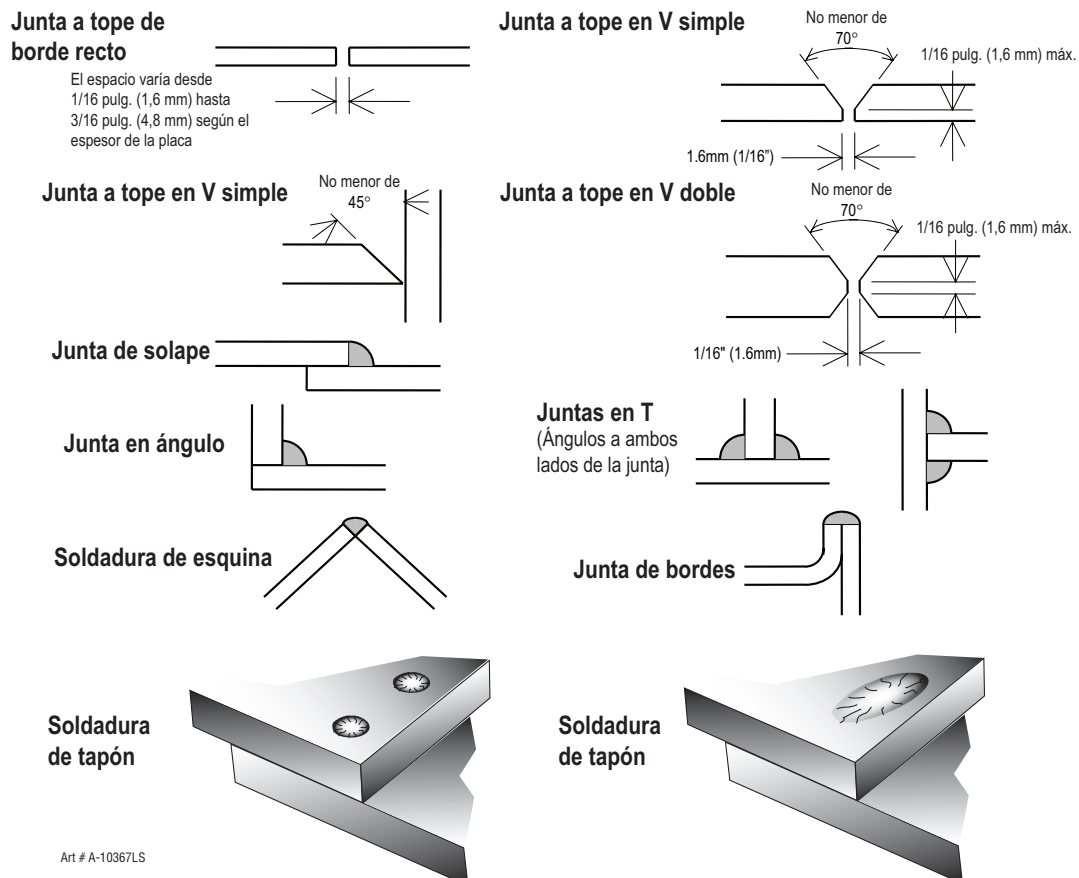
Diseños de junta típicos para la soldadura de arco
